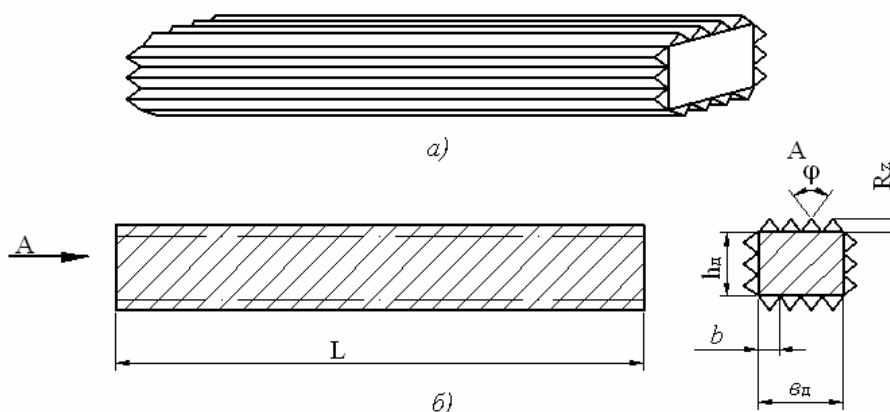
(а, б). Модель исходной шероховатости поверхности плоской детали из стали
